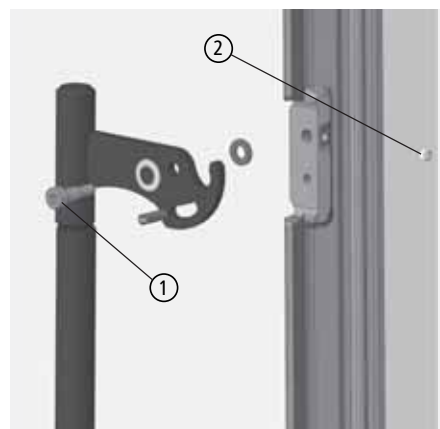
Türgriff, Befestigung mit Ansatzschraube, Madenschraube zur Sicherung
